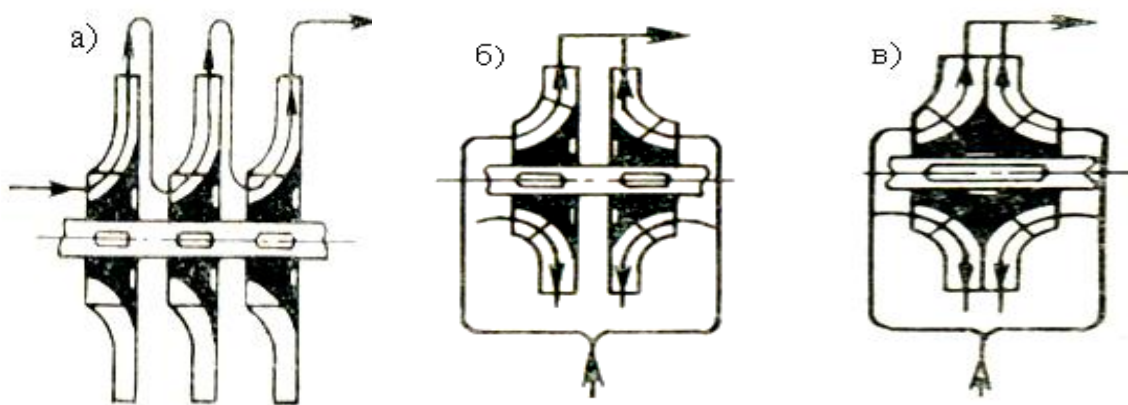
Схемы соединения рабочих колес центробежного насоса:
